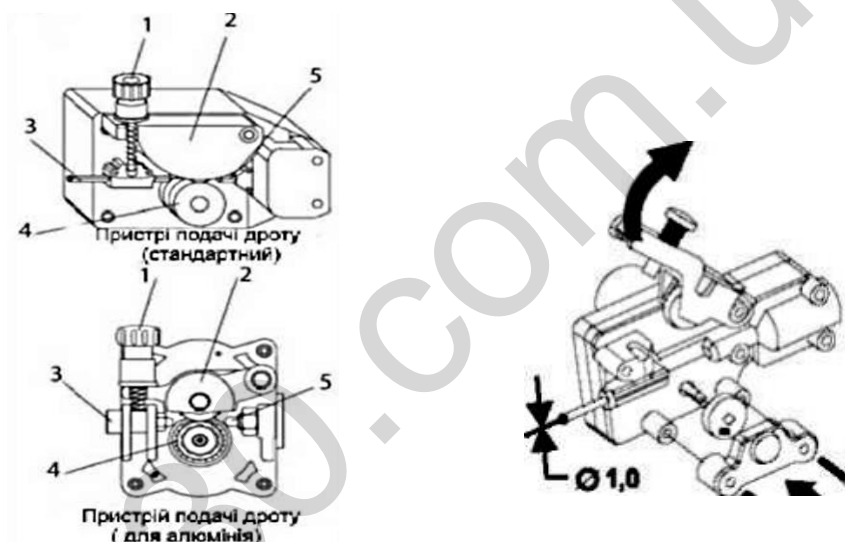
Установка сварочной проволоки в механизм протяжки
